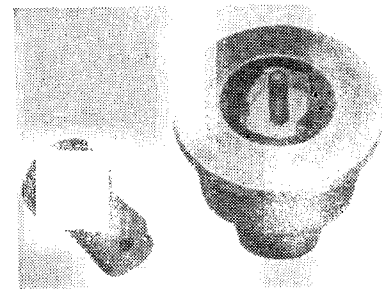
Прессформа для прессования спеченных магнитов, футерованная металлокерамическим твердым сплавом
